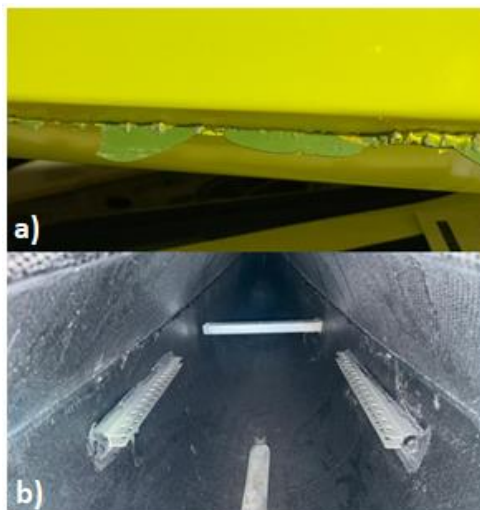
Aspecto da junta adesiva fabricada após o barco ser retirado do molde: (a) vista exterior, (b) vista interior
